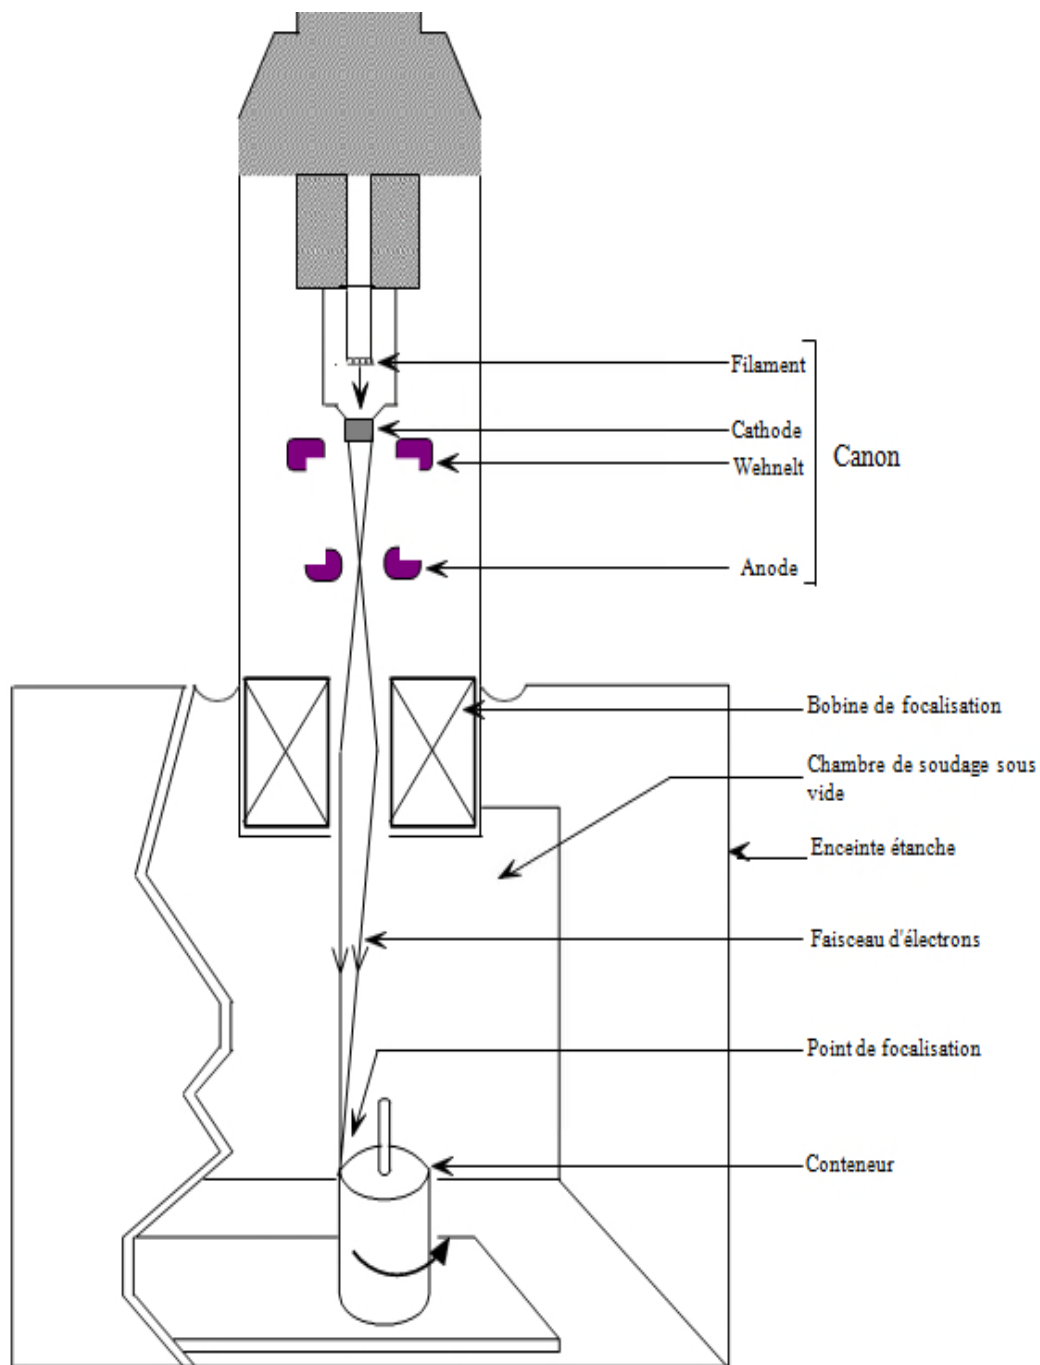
Schéma de principe de l'appareillage pour le soudage par bombardement électronique [2].
